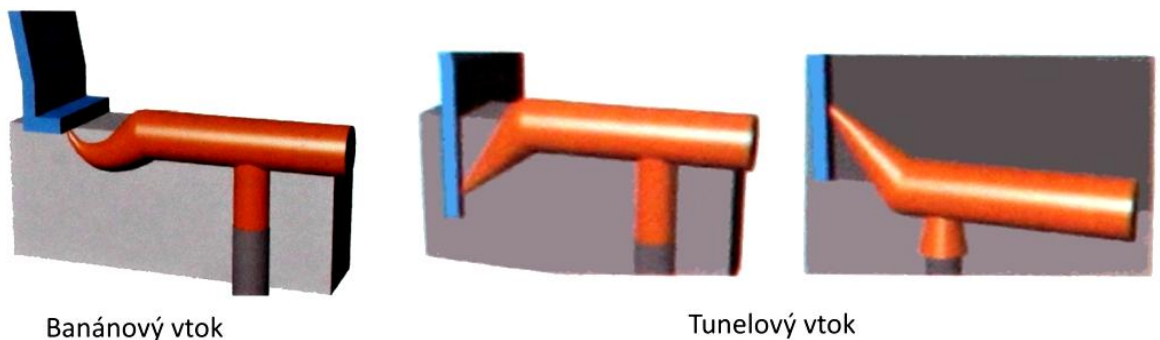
Rozdělení základních typů vtokových ústí [18]
